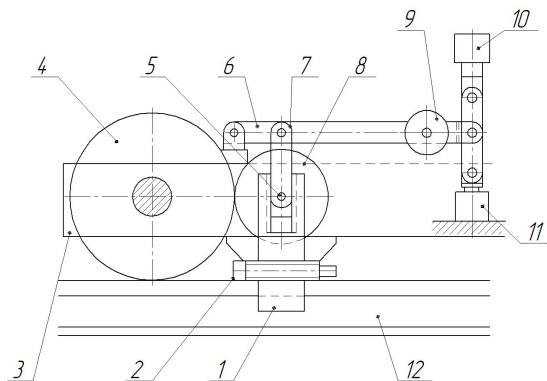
Автоматический рельсовый захват с электромагнитом: 1 – нижний конец рычага; 2 – обойма; 3 – рама; 4 – ходовое колесо; 5 – винт; 6 – рычаг; 7 – нижняя часть тяги; 8 – фрикционный диск; 9 – нажимной груз; 10 – электромагнит; 11 – гидравлический демпфер-замедлитель; 12 – рельс
